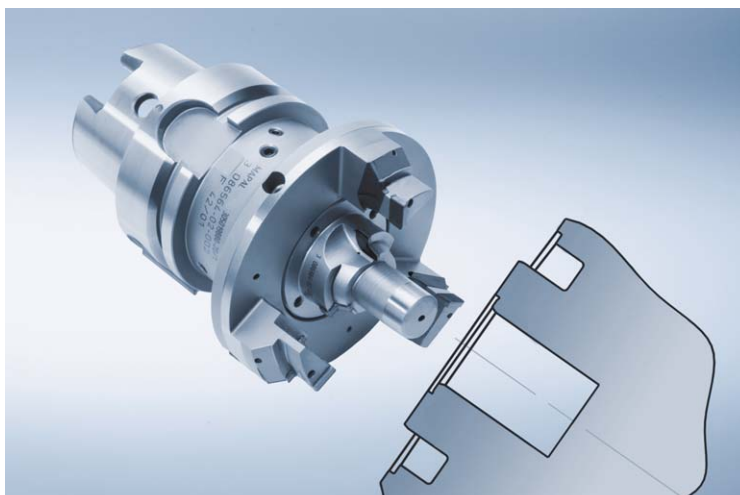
Aufwendige Konturen mit PKD-Werkzeugen prozesssicher und hochgenau bearbeiten – auch in Messing.
